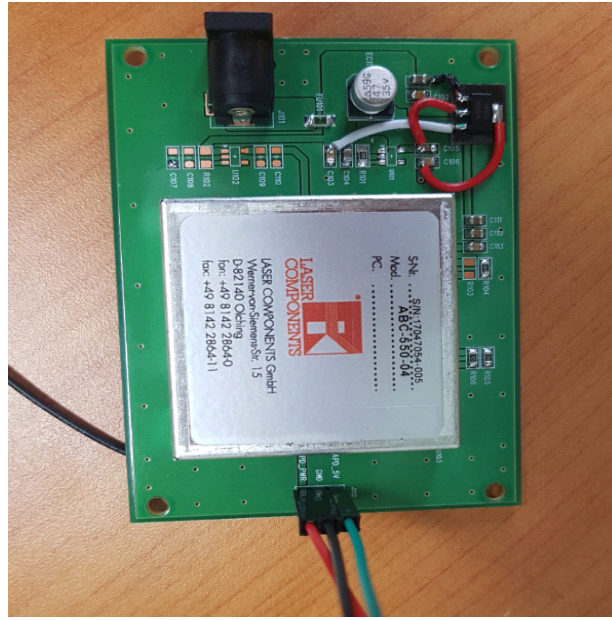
제작한 pcb를 적용한 전원장치
